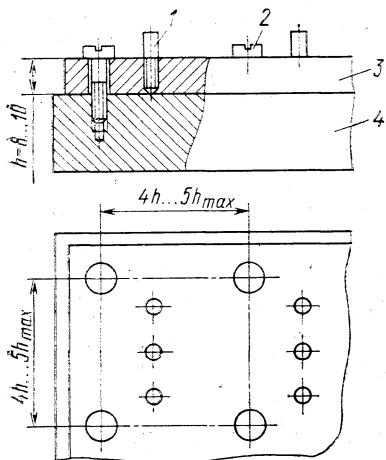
Рекомендуемый способ крепления монтажной платы к приспособлению:
